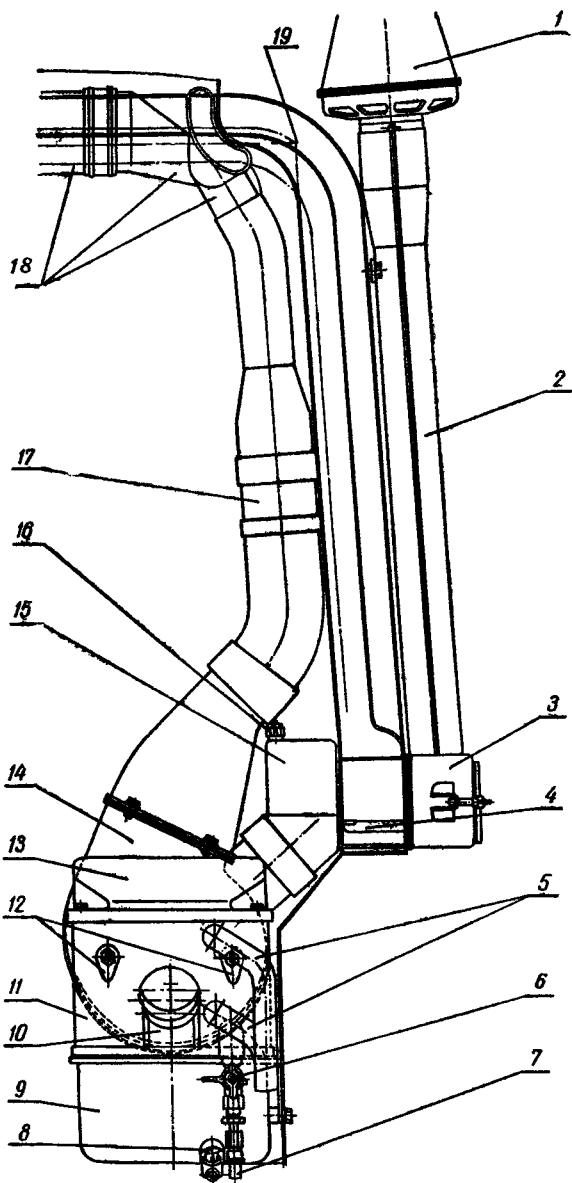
Блок отопления и охлаждения воздуха кабины:
